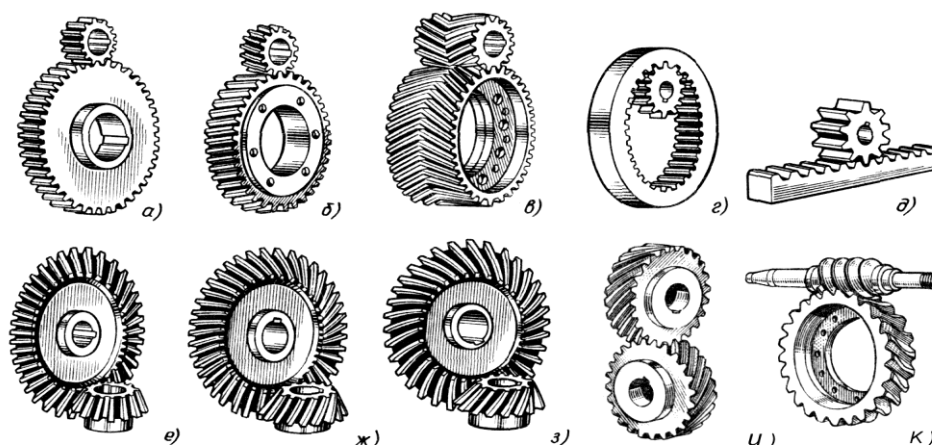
Виды зубчатых передач: а, б, в – цилиндрические зубчатые передачи с внешним зацеплением; г – цилиндрическая передача с внутренним зацеплением; д – реечная передача; е, ж, з – конические зубчатые передачи; и – винтовая передача; к – червячная передача.
